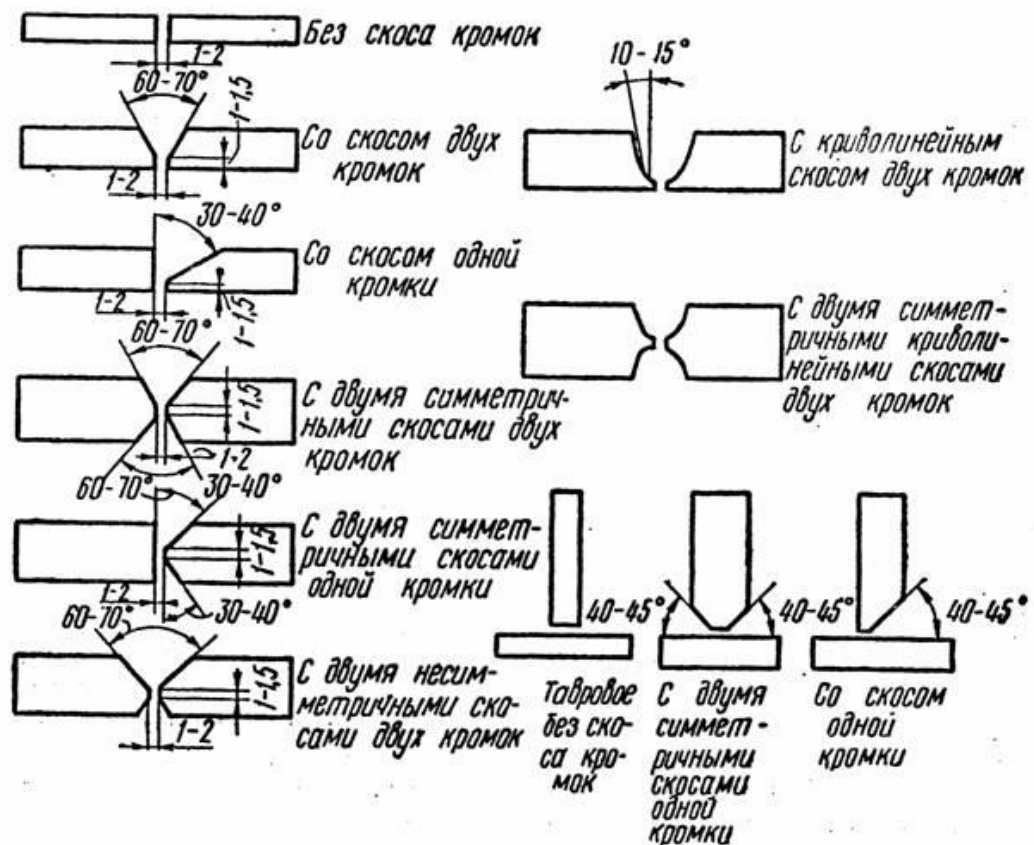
Виды подготовки кромок под сварку.
